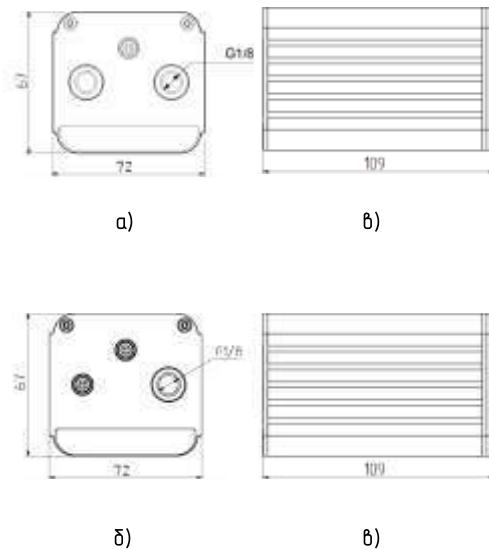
Габаритные размеры преобразователей давления конструктивного исполнения 3.
